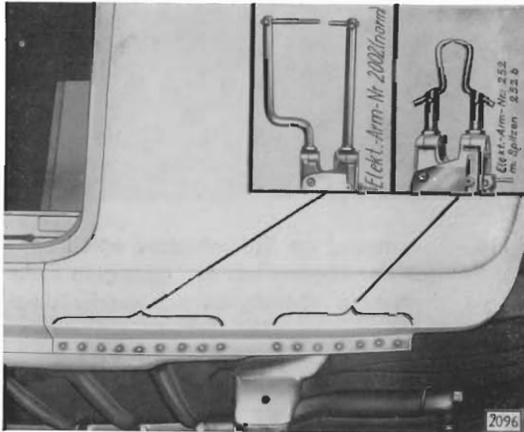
Seitenwand an Bodenblech und zusätzlichen Haltewinkel des Bodenbleches zangenpunktgeschweißt
